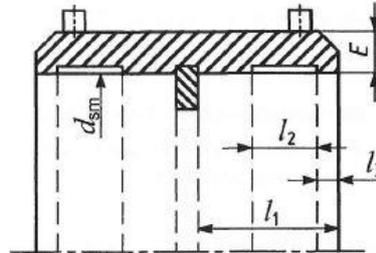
Heizwendelschweißmuffe (Elektroschweißmuffe)
